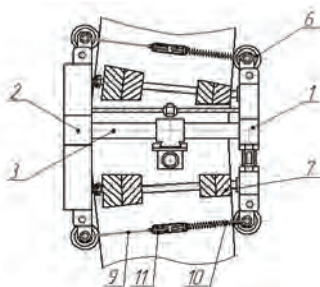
Передвижной станок для обработки торцов крупногабаритных деталей
